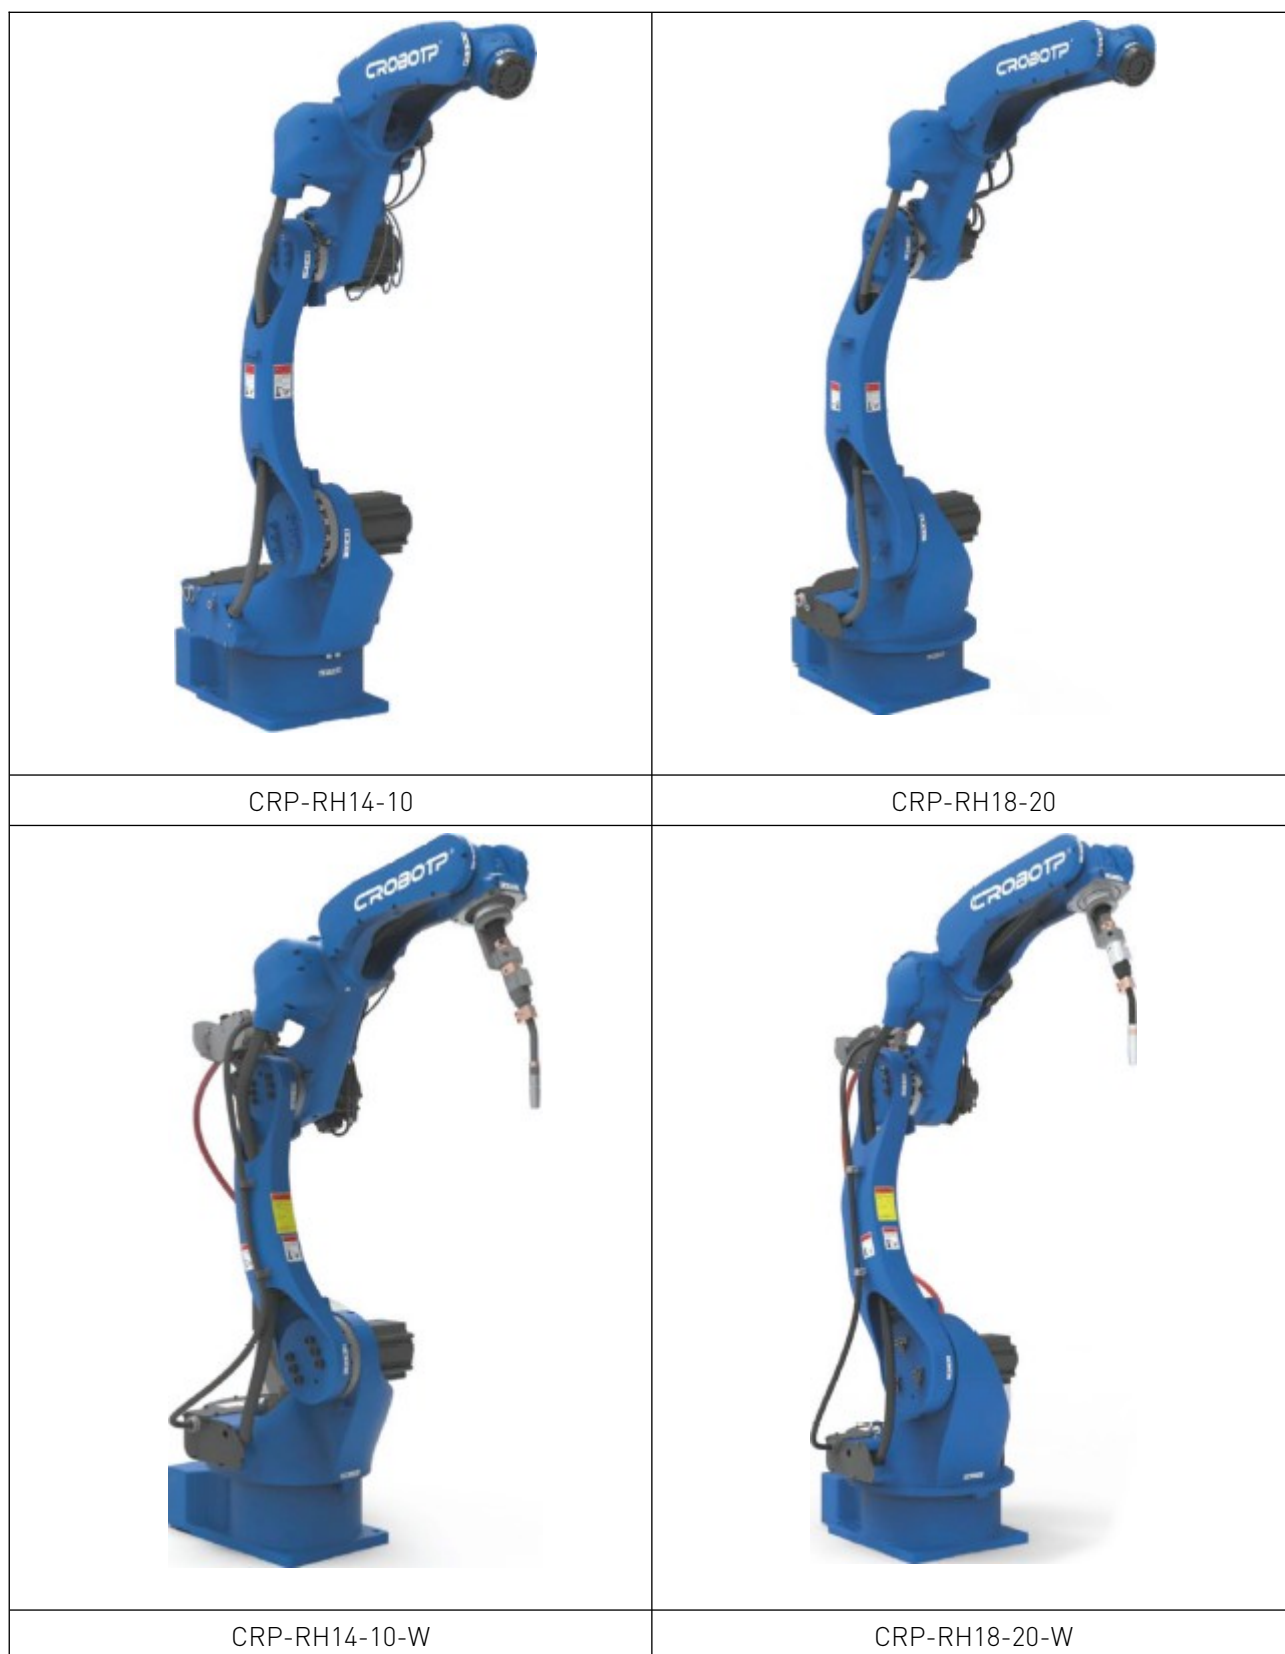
Роботы-манипуляторы CRP, сварочные роботы CRP (W).
